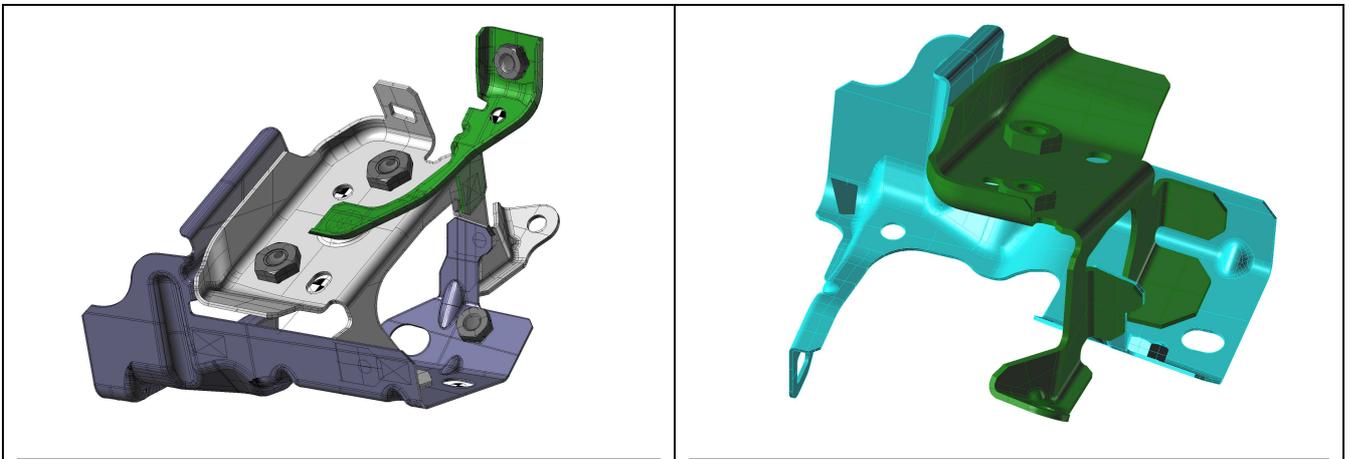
Staffa fiss. cerniera fissa e tergi DX-SX
